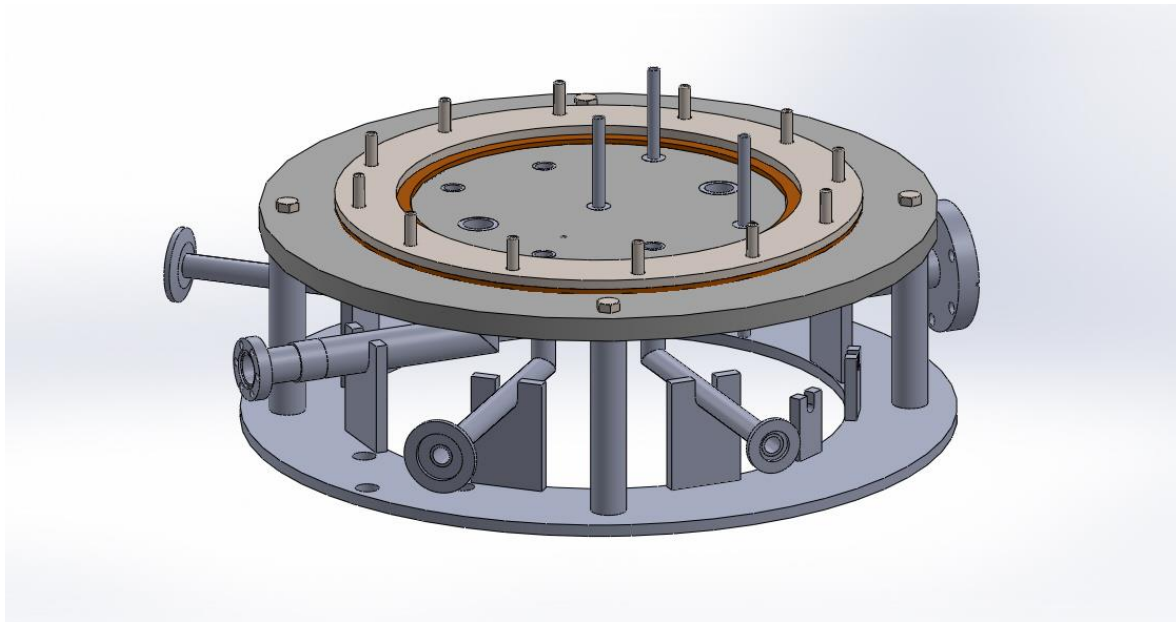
Vista dimétrica del ensamble de la brida de aluminio.
